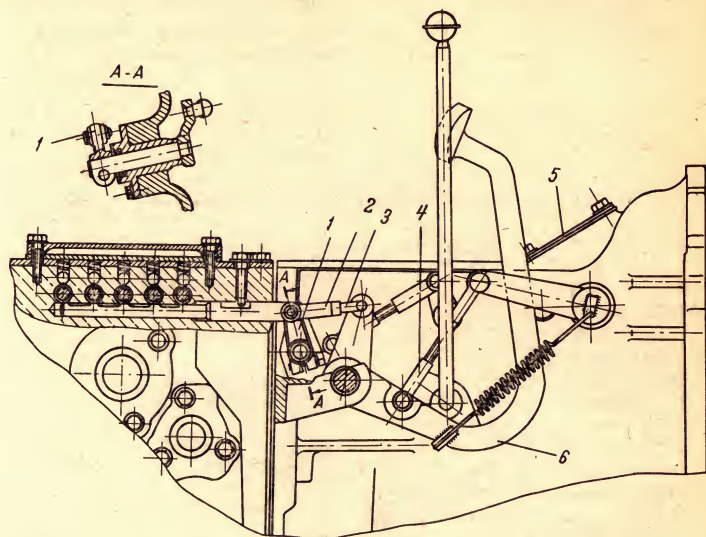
Привод муфты сцепления и механизма блокировки коробки передач тракторов Т-40М и Т-40АМ:
